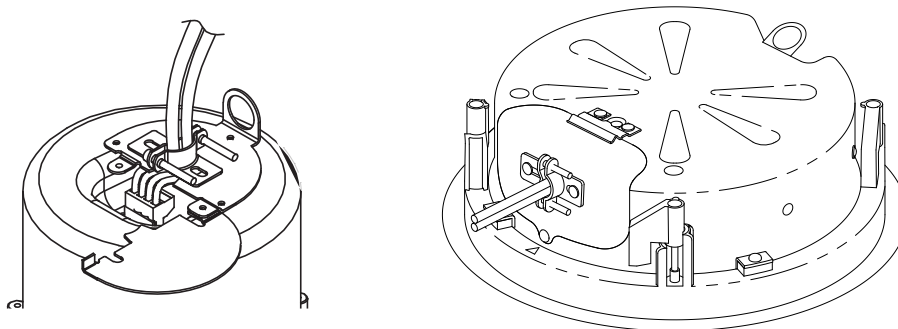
Befestigen Sie das Kabel durch die Verschaubung außer C4.2LP (links); befestigen Sie das Kabel durch die Verschaubung für den C4.2LP (rechts)
